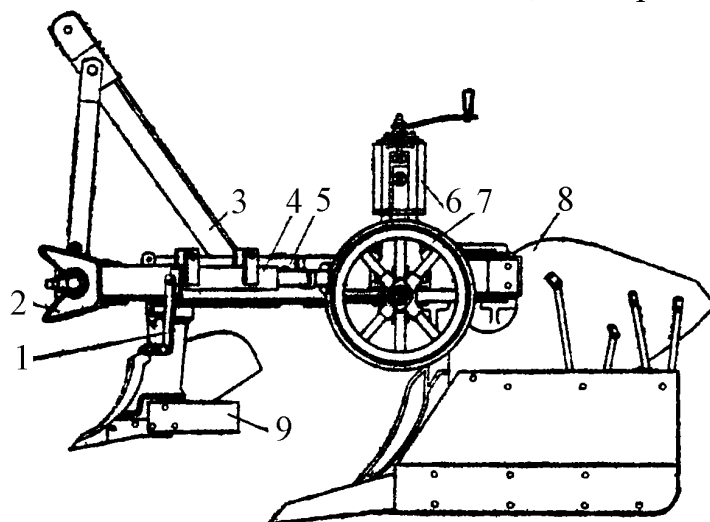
Плуг плантажный ППН-50: 1 – стойка; 2 – вилка; 3 – навесная система; 4 – винтовой механизм; 5 – рама; 6 – винтовой механизм опорного колеса; 7 – опорное колесо; 8 – основной корпус; 9 – предплужник
